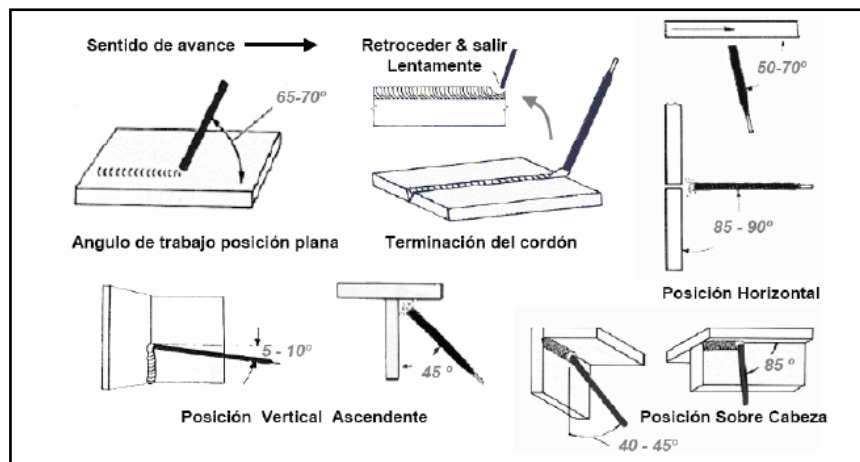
Técnicas de soldadura. (ESAB 2010).
